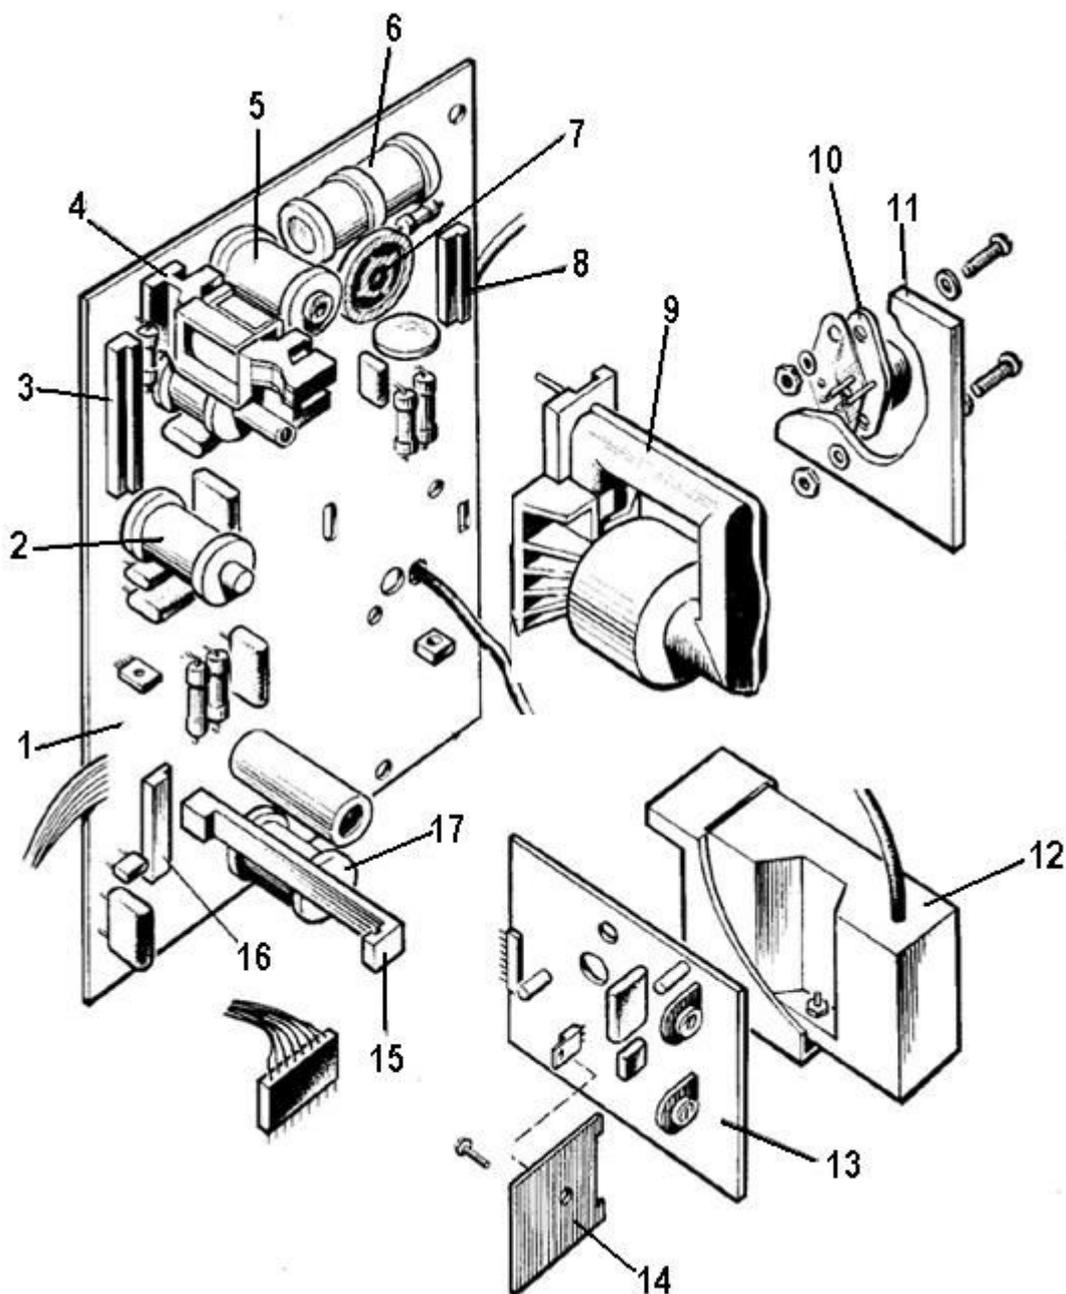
Внешний вид конструкции модуля строчной развертки МС-3
